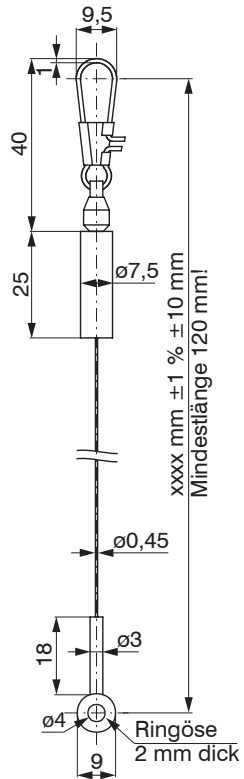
Seilverlängerung WE-xxx-CLIP, Abmessungen in mm
